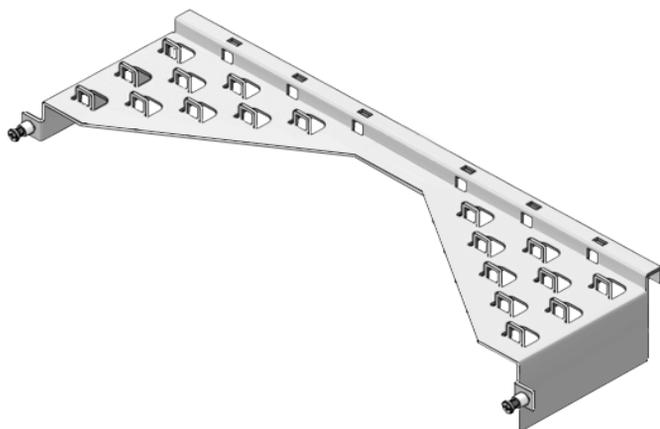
Vue supérieure de la plaque de gestion des câbles de type A
